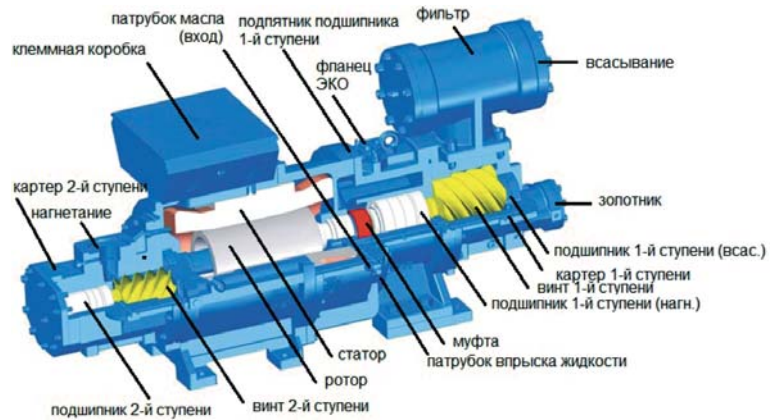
Низкотемпературный двухступенчатый винтовой компрессор в разрезе
